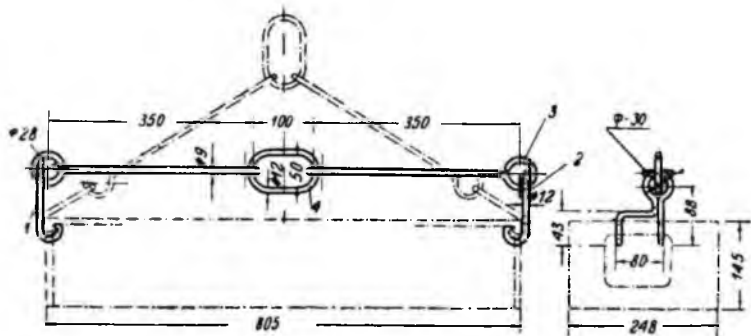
Схватка для головки цилиндров двигателя СХТЗ-НАТИ.
